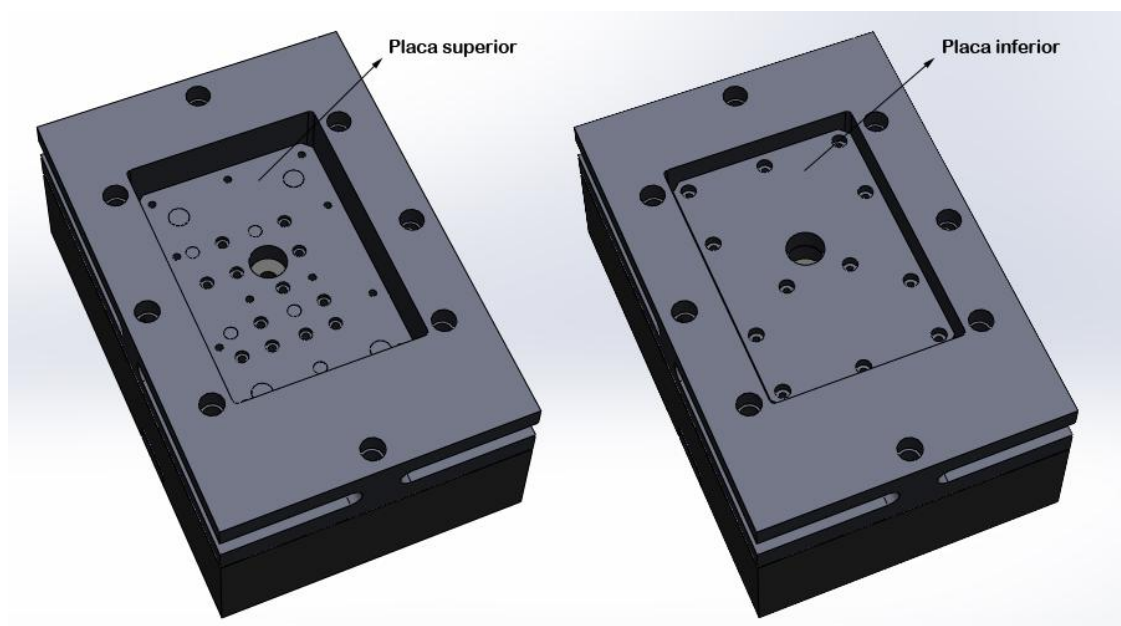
Placa de expulsores acoplada al molde de acero.
